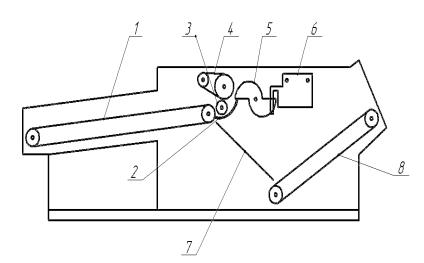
Конструктивная схема режущего станка РМО-1: 1-крепежная лента; 2 - стольник; 3 - зажимной валик; 4-направляющая лента; 5 - режущий нож; 6 - неподвижная расческа; 7-жалюзи; 8-выпускная лента.
